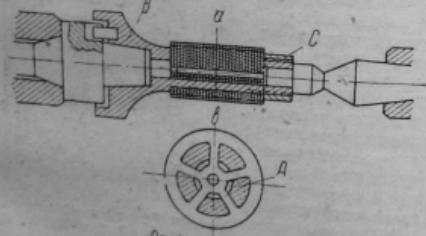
Револьверный автомат Ламберт для обточки барабанов.
